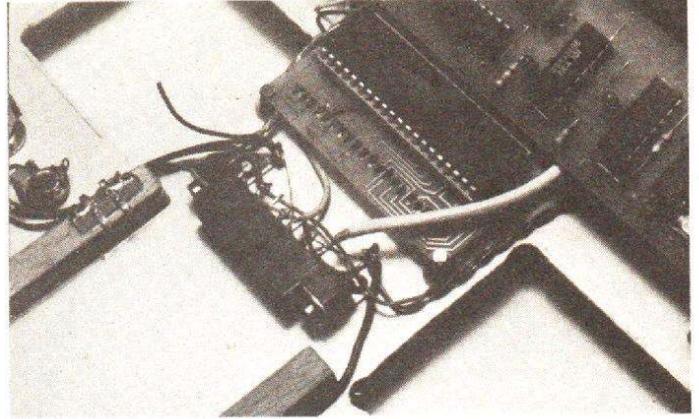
Photo I. - Détail montrant les lamelles de contact du 5^e digit, sur la glissière gauche.
